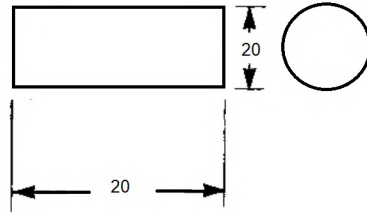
Dimensiones probeta cilíndrica para compresión
